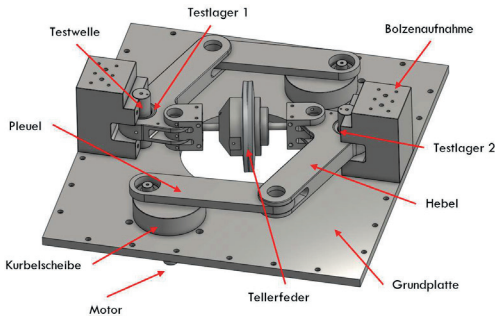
Hauptmaschinenkomponenten des Kniehebelteststandes
